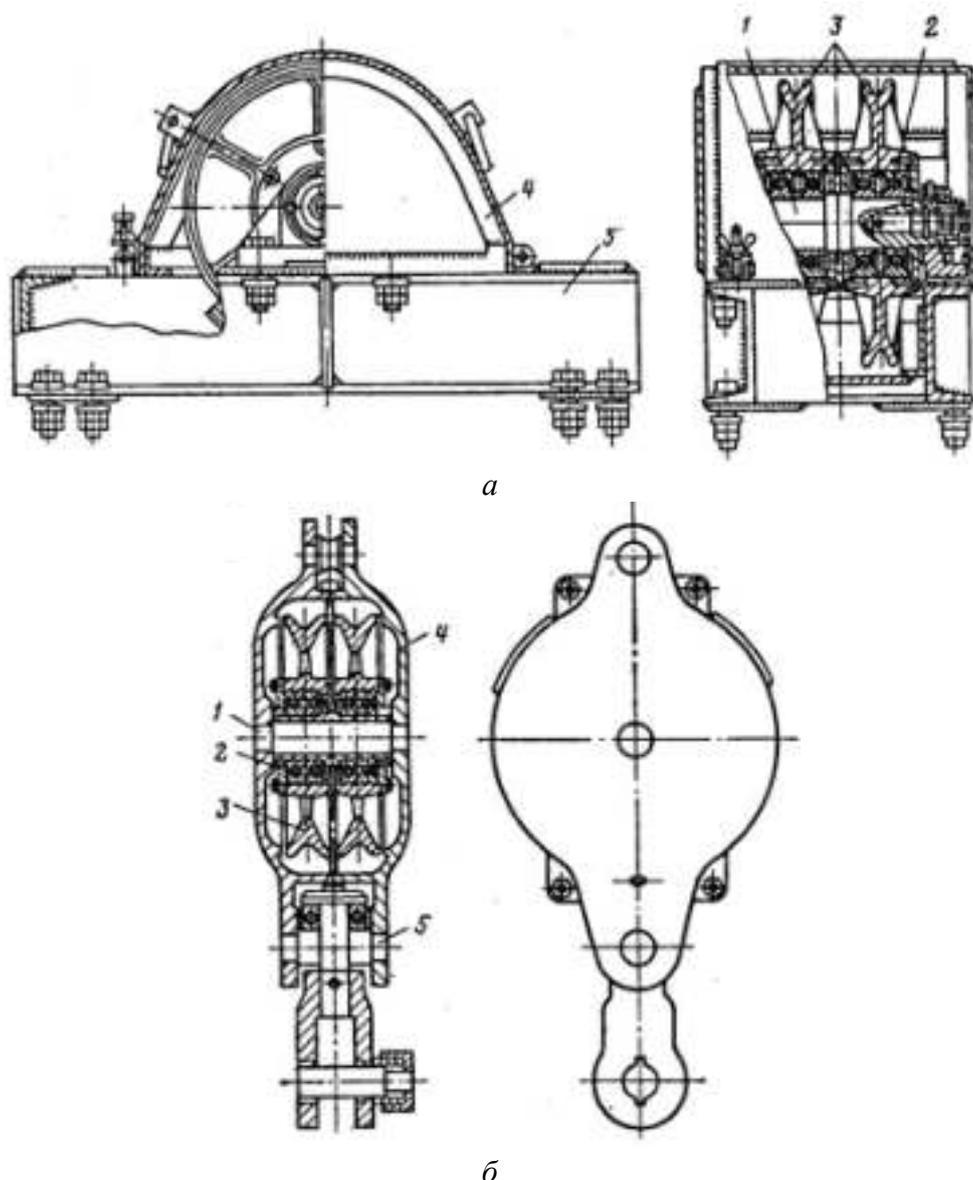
Талевая система: *а* – кронблок: 1 – валик; 2 – подшипник; 3 – шкивы; *б* – талевый блок: 1 – валик; 2 – подшипник; 3 – шкив; 4 – корпус; 5 – ось
